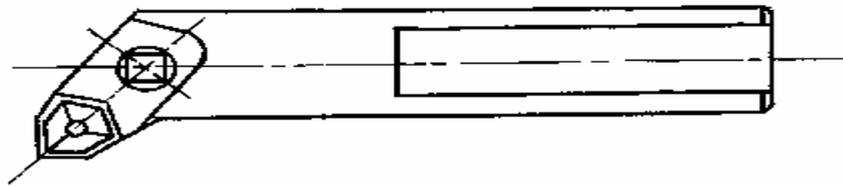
Резец токарный сборный расточный с механическим креплением трехгранных пластин из твердого сплава (К.01.4261.000)
